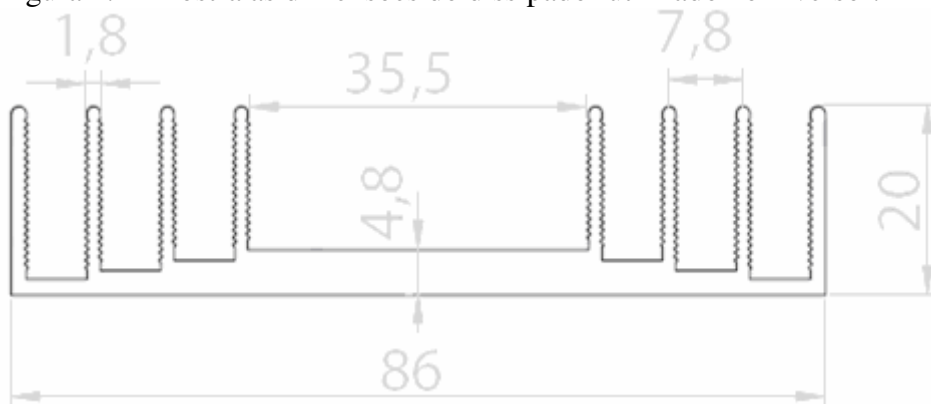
Dimensões do dissipador utilizado no inversor (20 x 86x 160 mm)
